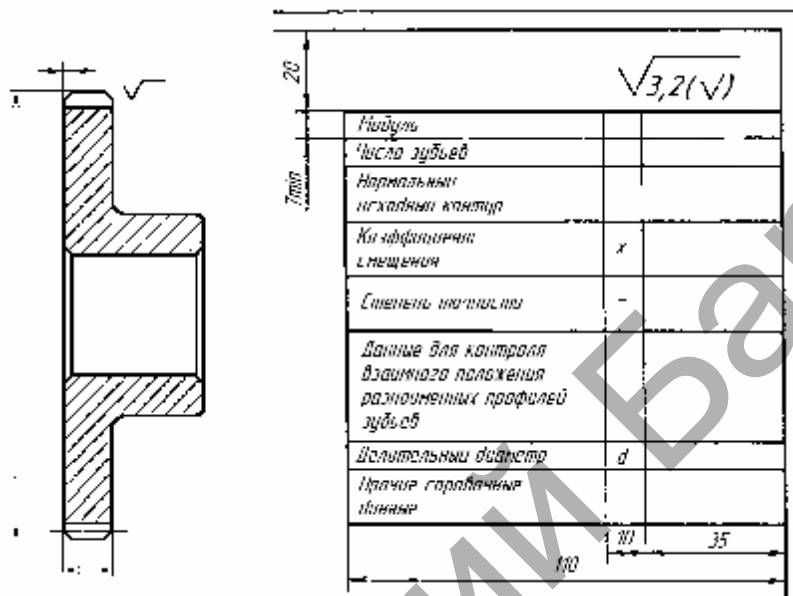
Пример указания параметров зубчатого венца на чертеже прямозубого цилиндрического зубчатого колеса со стандартным исходным контуром по ГОСТ 2.403
